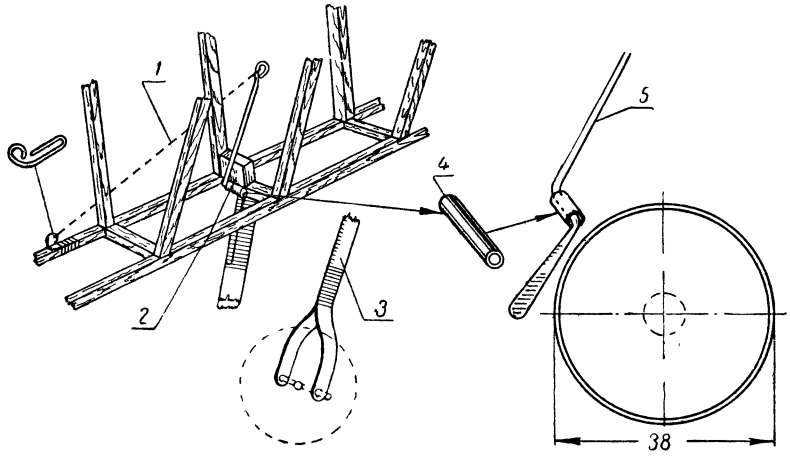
Передняя бобышка, подшипник и складывающийся винт.
